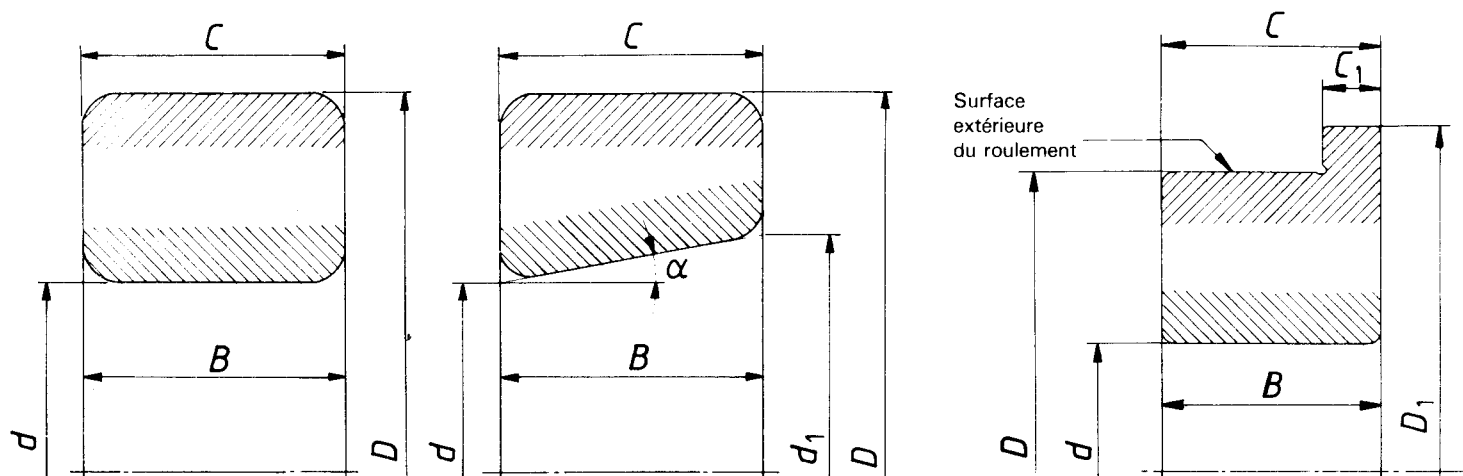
Symboles relatifs aux dimensions d'encombrement
